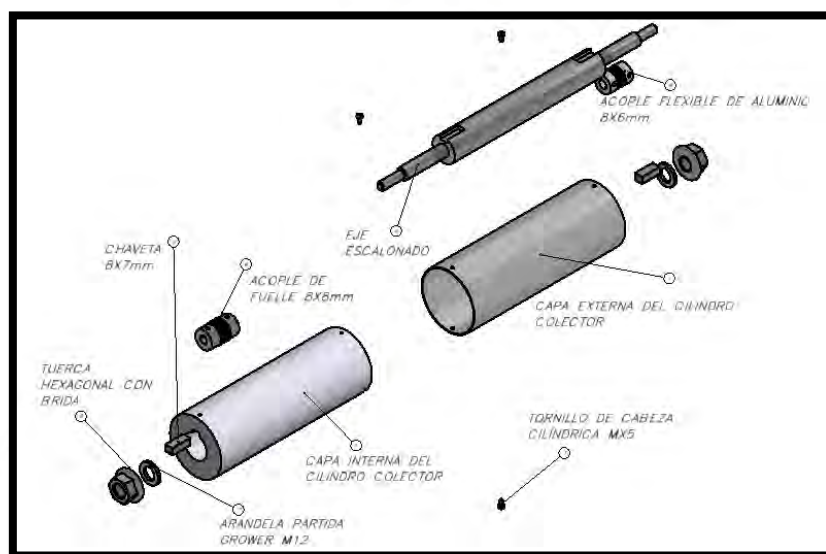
Vista de explosión del cilindro colector y los componentes mecánicos que permiten la transmisión del movimiento giratorio.
